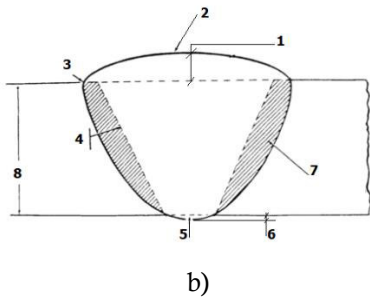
Geometrias de bordos de juntas de soldadura [80]
